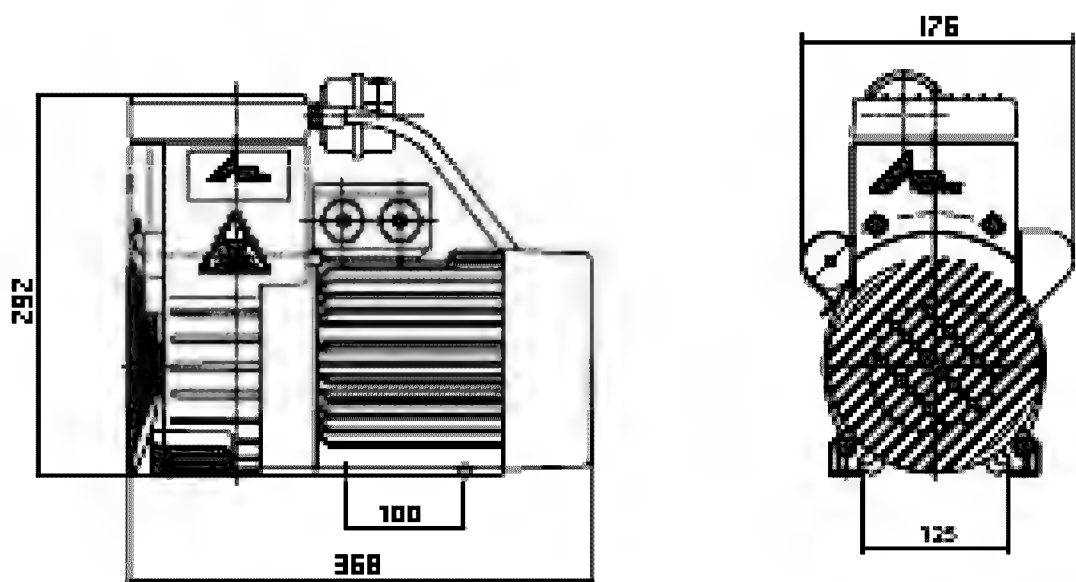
Габаритные и присоединительные размеры компрессора D-100
